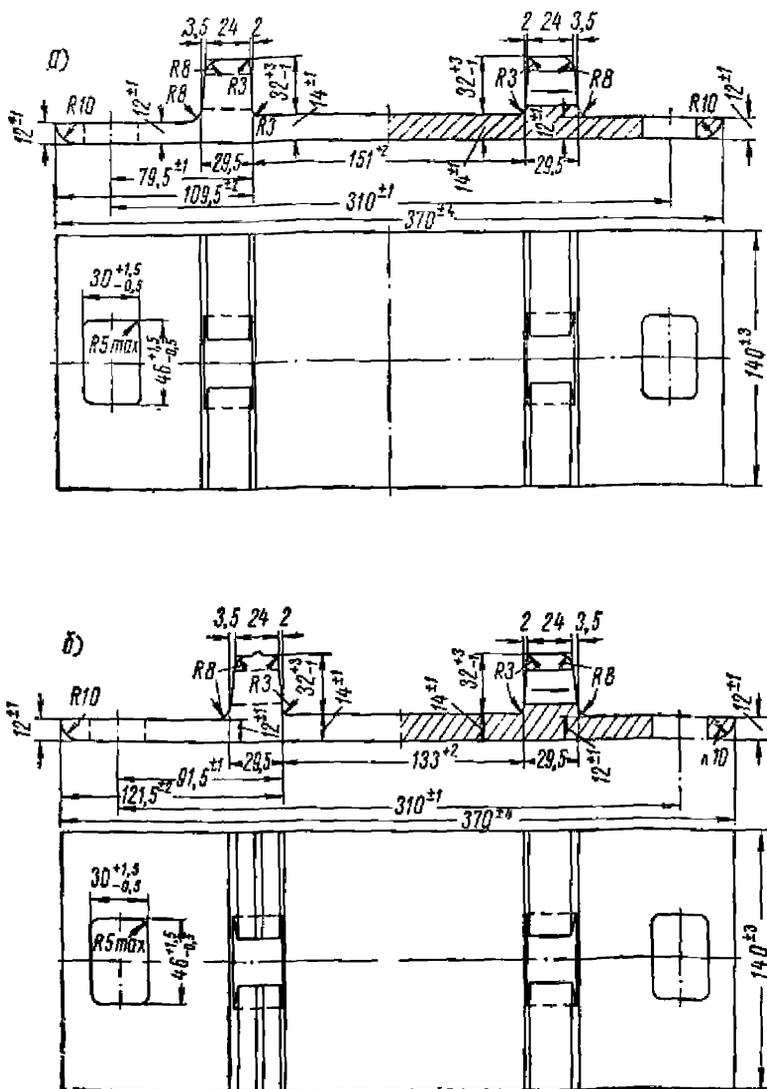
Подкладки марки К плоские с болтовым креплением к железобетонной шпале:
